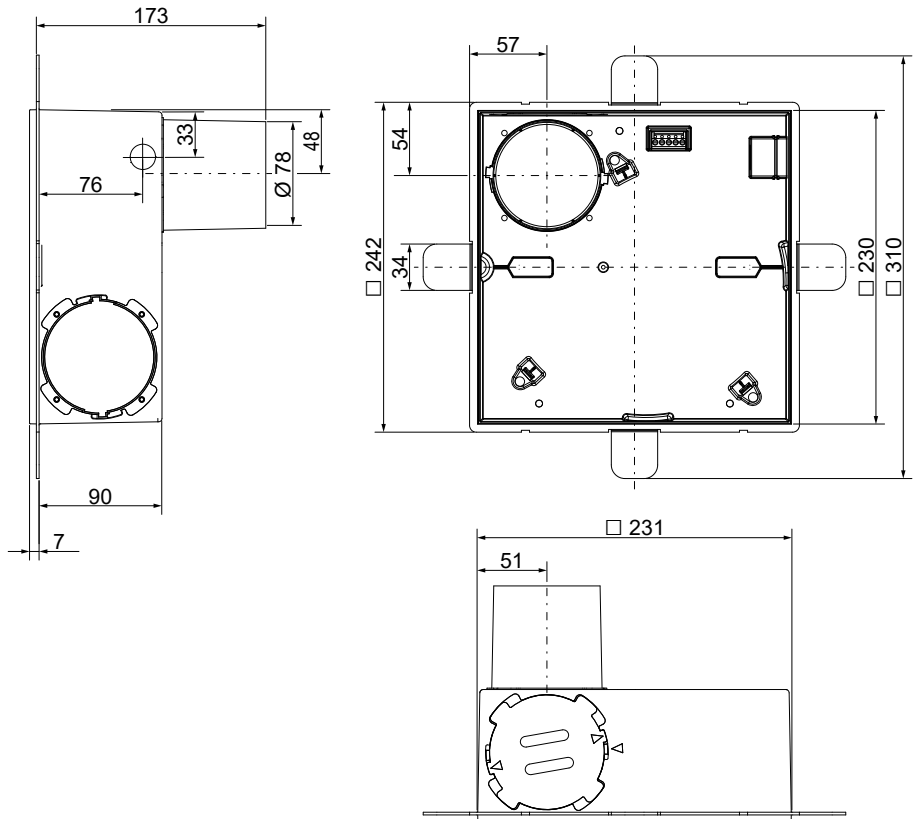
Maßzeichnung – Gehäuse Abluftventilator Taris UP axial
